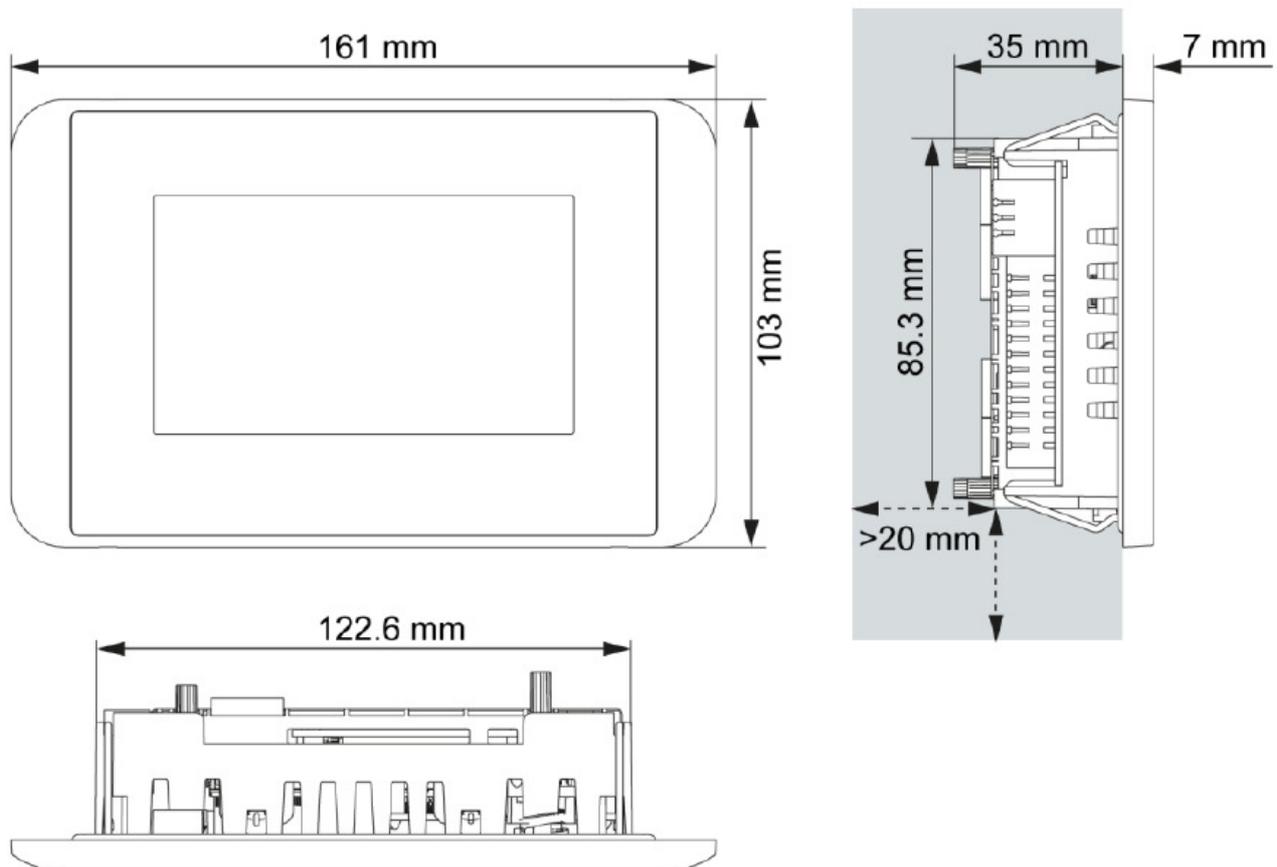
Габаритные размеры контроллера DC2004
